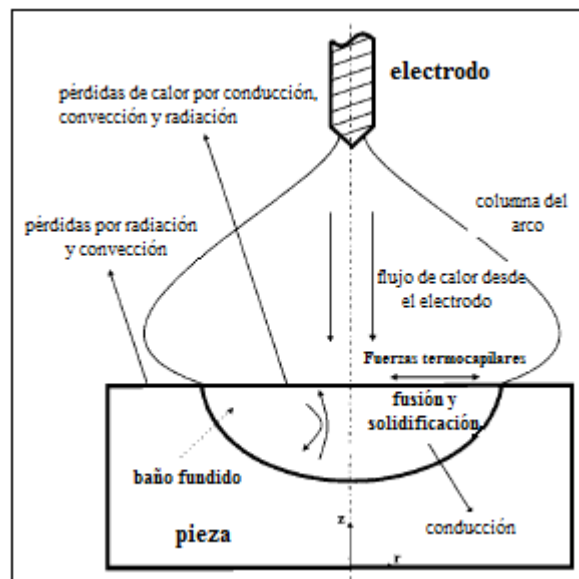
Esquema del modelo típico de un proceso de soldadura
